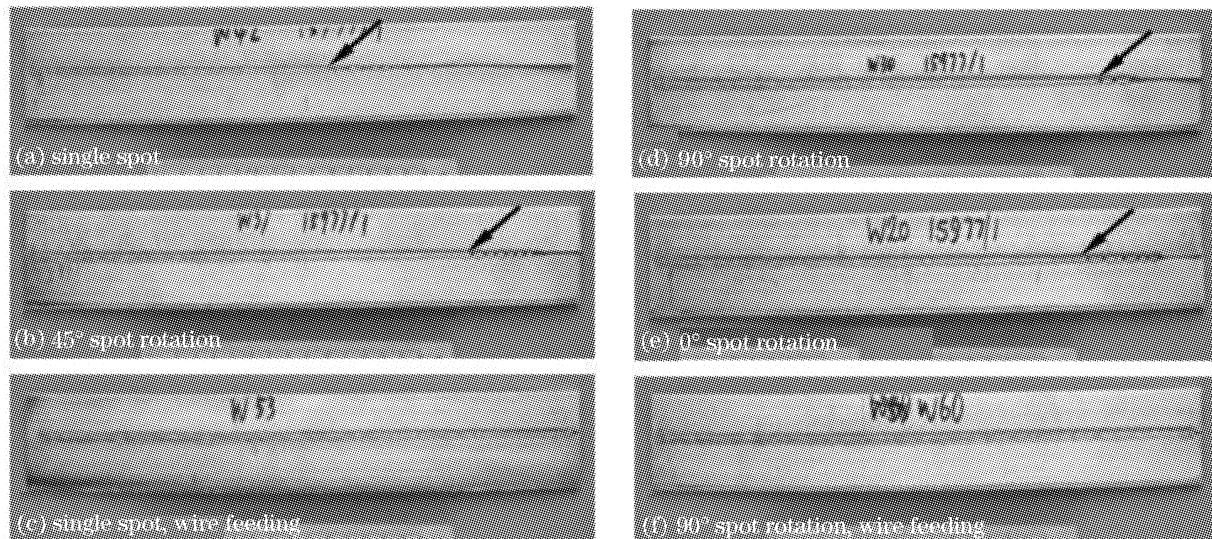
0~1 mm 变间隙对接焊焊缝的外观形貌
